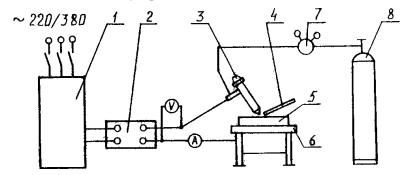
Схема установки для сварки алюминия в среде аргона: 1 – трансформатор; 2 – осциллятор; 3 – газозлектрическая горелка; 4 – присадочный пруток; 5 – деталь; 6 – стол сварщика; 7 – редуктор-расходомер; 8 – баллон с газом
